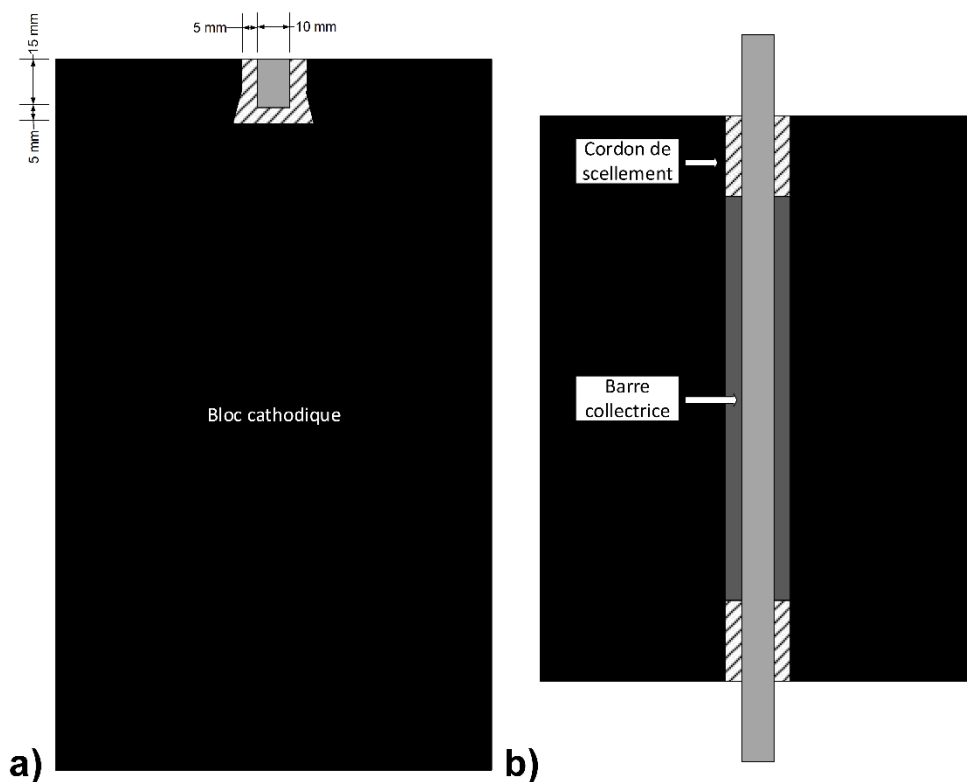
Assemblage de la barre collectrice avant le scellement a) vue de côté b) vue du dessus
